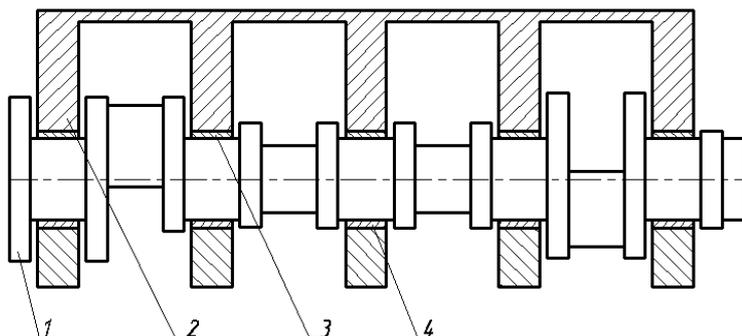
Схема многоопорного узла поддержки коленчатого вала: 1 – коленчатый вал, 2 – картер, 3 – верхний коренной вкладыш, 4 – нижний коренной вкладыш
